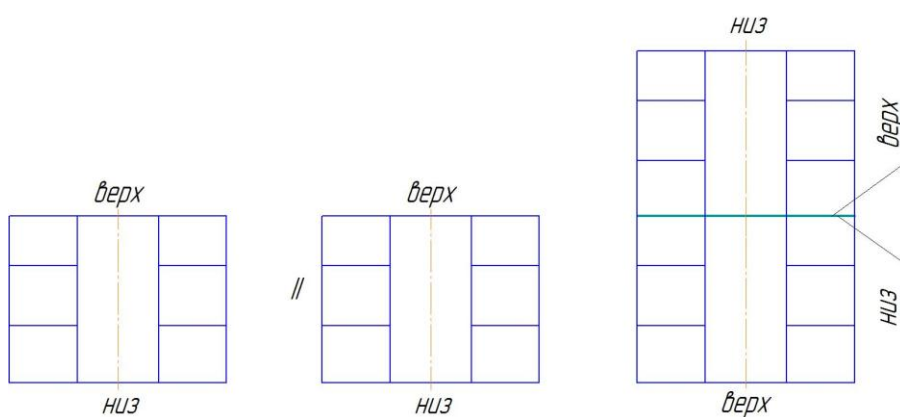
Схема сборки пакета перед окончательным прессованием
